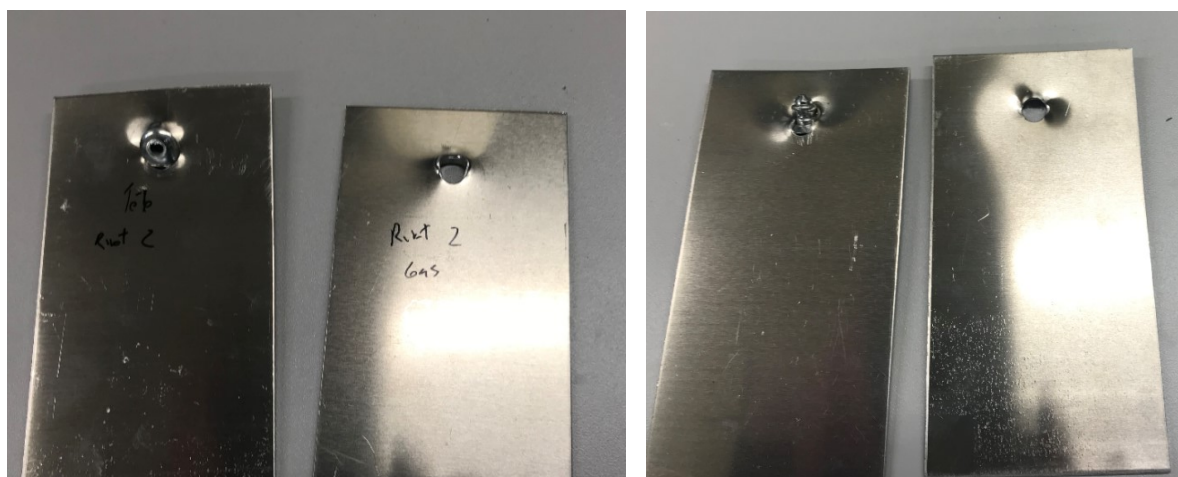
Bris typique des joints rivetés de la série 1 (recouvrement)Figure 33 : Bris typique des joints rivetés de la série 2 (recouvrement)
